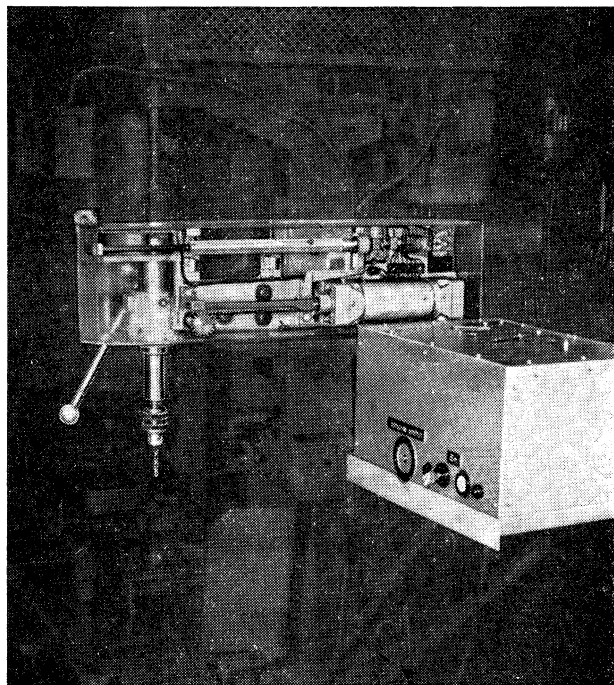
Steuereinrichtung für Bohrmaschinen
